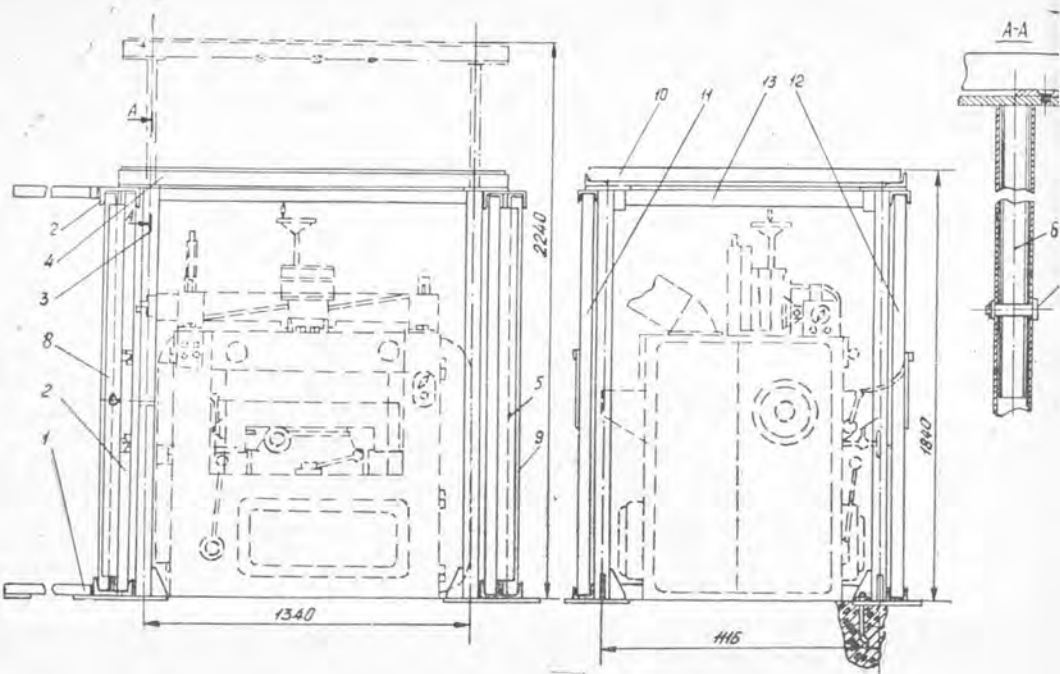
Звукоизолирующий кожух реймусового станка с выдвижными щитами.
